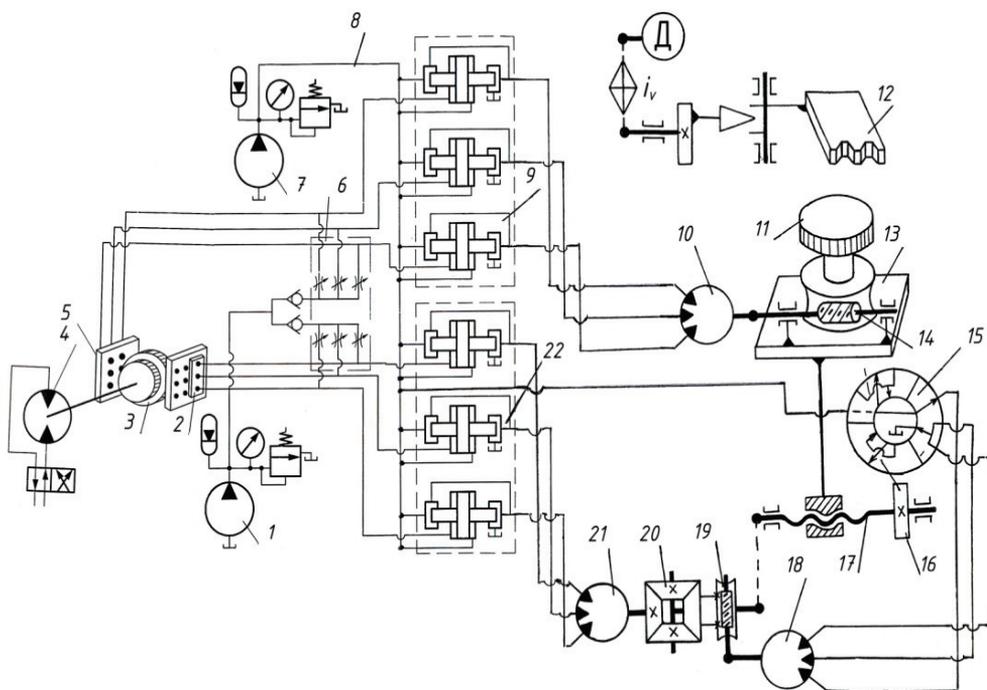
Структурная схема зубострогального станка с внутренними гидравлическими связями для нарезания зубьев цилиндрических зубчатых колес зуборезной гребенкой
